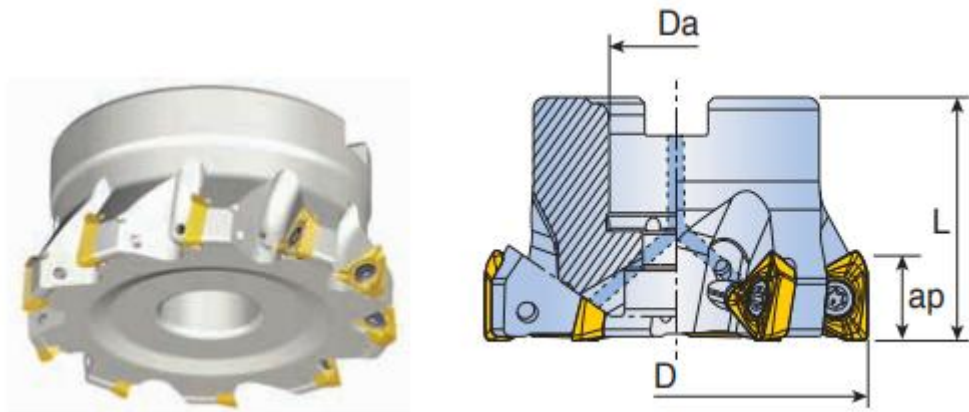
Торцева фреза Mill Rush 3P TF90 фірми Taegutec
